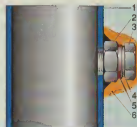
Ремонт амортизатора: 1 — корпус; 2 — гайка (приваривается); 3 — болт-пробка; 4 — шайба; 5 — резиновая прокладка; 6 — герметик.
